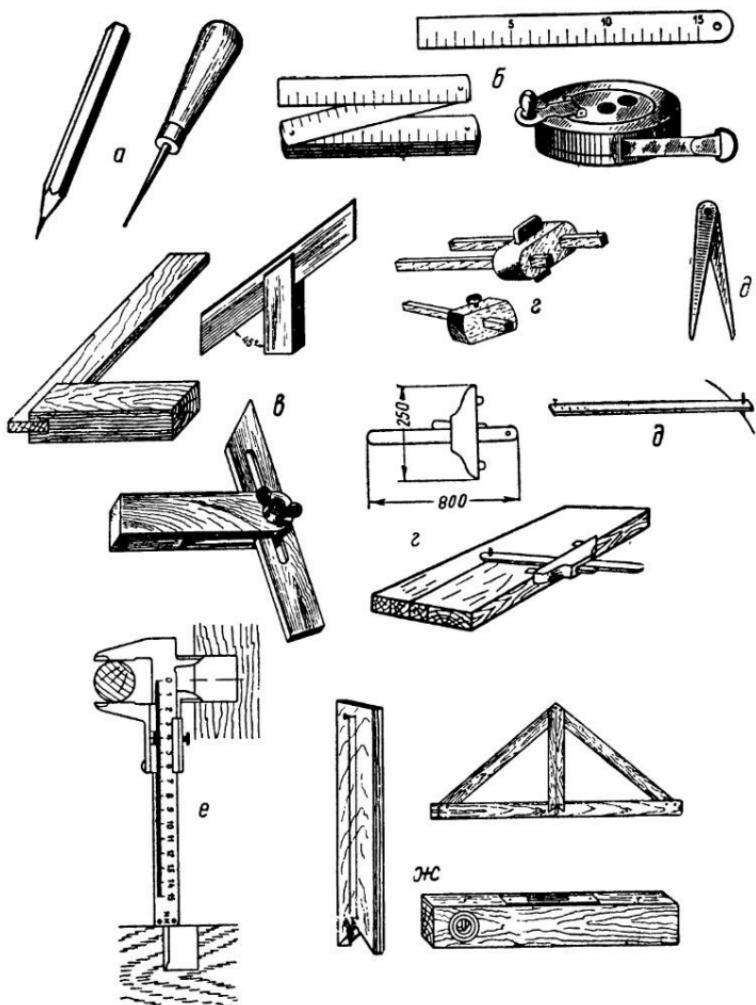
Разметочный инструмент: а — карандаш и шило; б — линейка, метр и рулетка; в — угольник, ярунок и малка; г — рейсмусы, обычные и щитовой; д — циркуль и реечный циркуль; е — штангенциркуль; жс — отвесы и уровень.
